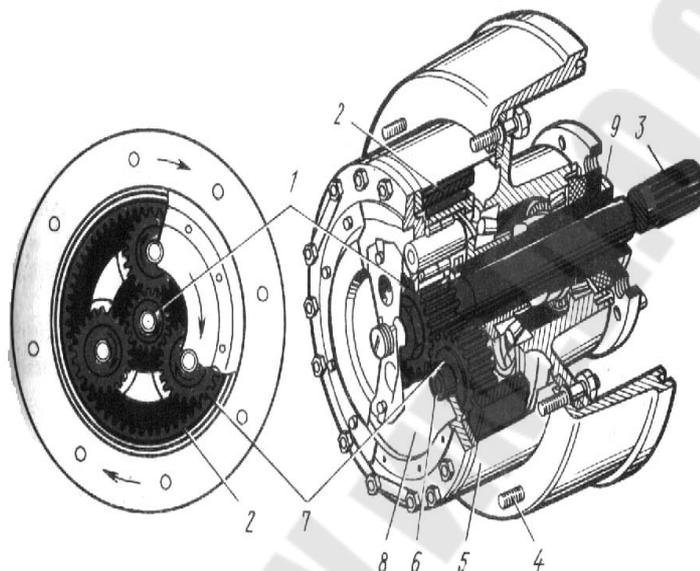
Колесный редуктор трактора Т-150К
